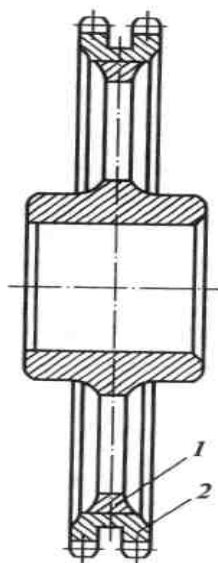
Ремонт цепного колеса способом замены части детали: 1 - цепное колесо; 2 - зубчатый венец
